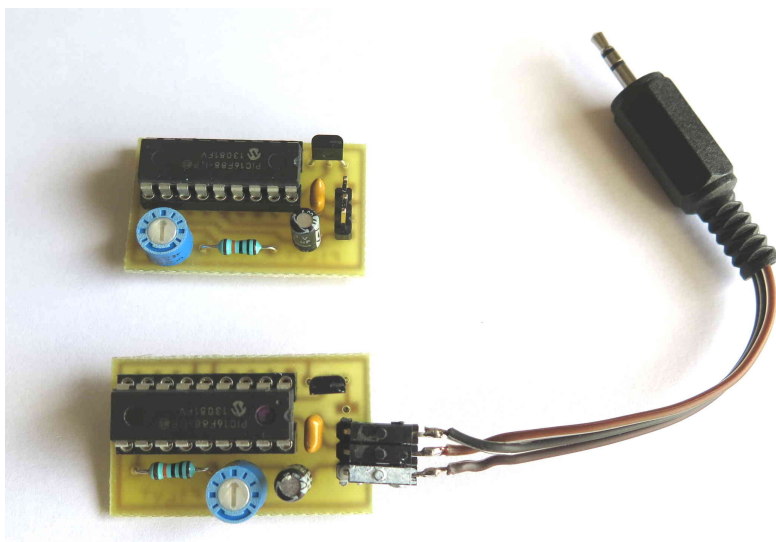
Le montage additionnel, autoalimenté par le TX LPD.
